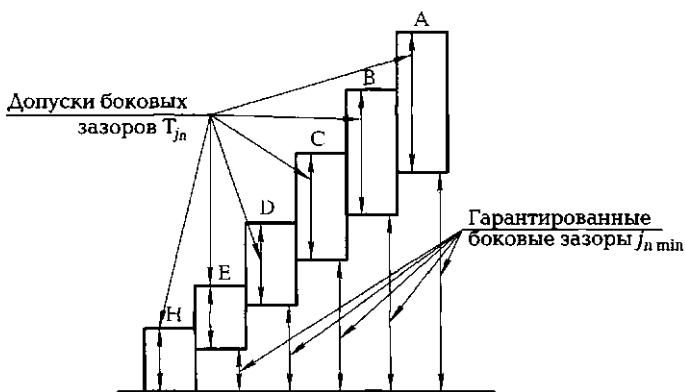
Виды сопряжений и допусков на боковой зазор
